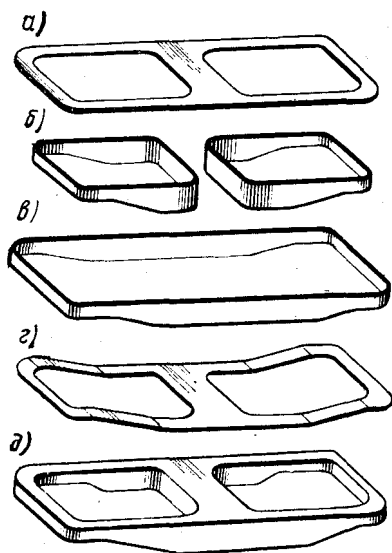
Сборочно-сварочные рации при изготовлении рамы тележки
